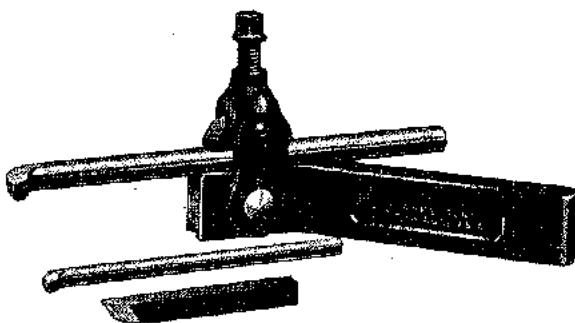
Herramientas de mandrinar con su soporte (Armstrong Bros. Tool Co.).
